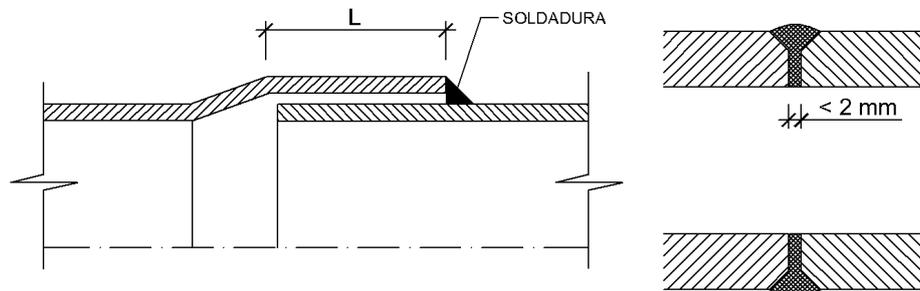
Detalle de unión abocardada (izquierda) o soldada a tope (derecha) en tubos de acero
